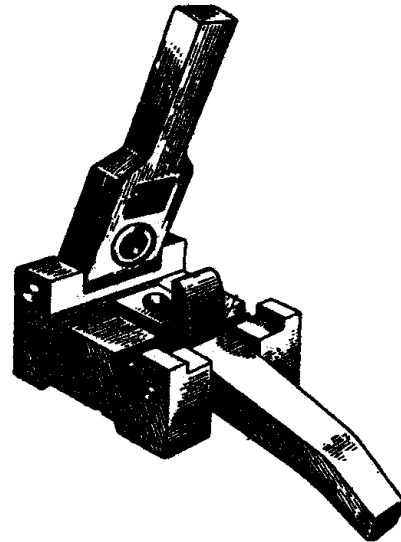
Кондуктор для свердління контакту фасонного перерізу.
